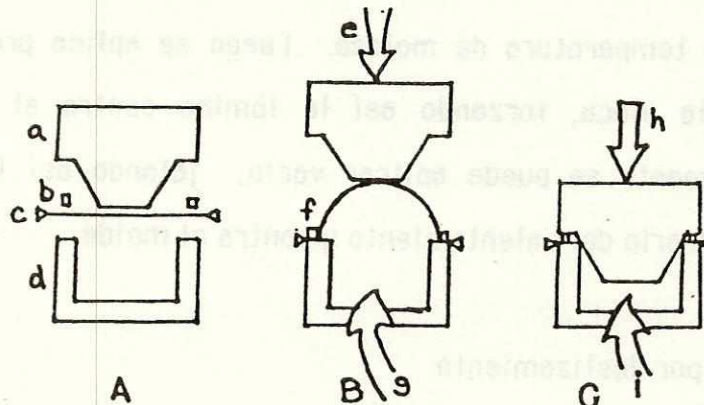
Formado por inmersión en una burbuja de presión de aire. A: Lámina precalentada previo al formado. B: Molde macho penetra la burbuja. C: Se aplica presión de aire para forzar la lámina en contra del molde macho. a: Molde macho. b: Anillo sujetador. c: Lámina precalentada y sujeta. d: cajón de presión. e: Molde macho penetra la burbuja. f: Lámina sujeta para contener la presión de aire interna. g: Presión de aire. h: Molde macho hace sello con anillo sujetador. i: Continúa la presión.
